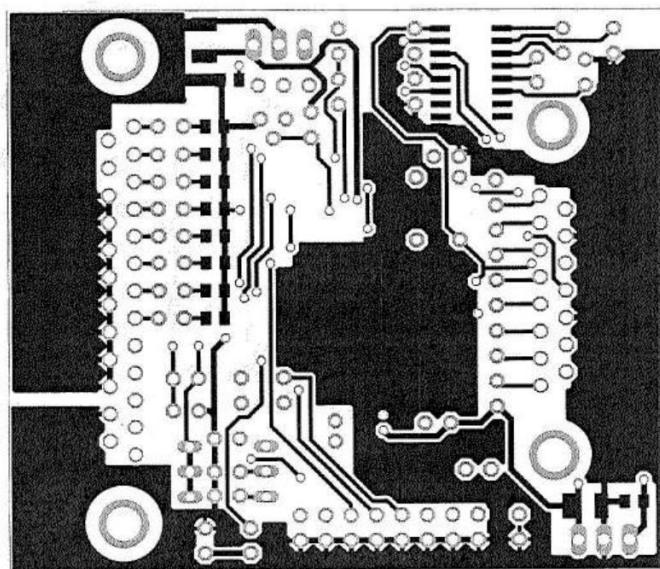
PCB:Tarjeta de adquisición, capa inferior.
